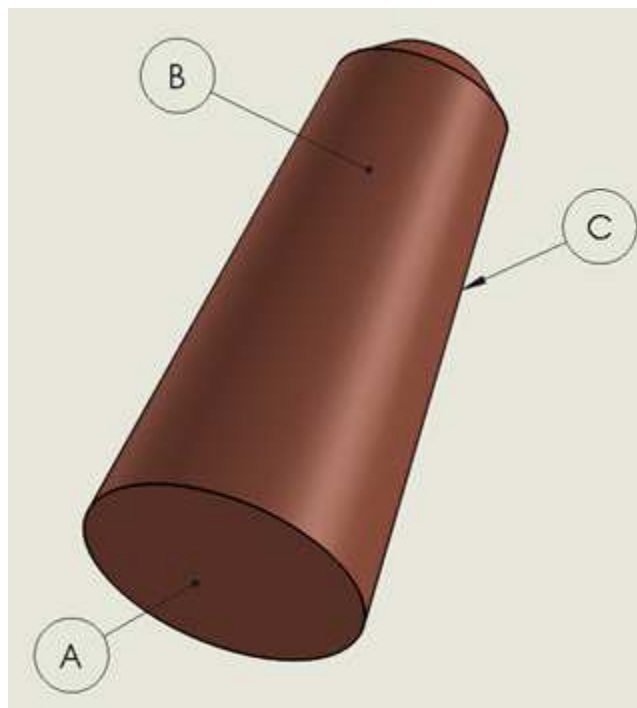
Desenho esquemático de um eletrodo de soldagem a ponto de componentes de ligas de zircônio, em destaque Face de soldagem (A), Corpo (B) e Conexão (C) [Fonte: o Autor].
